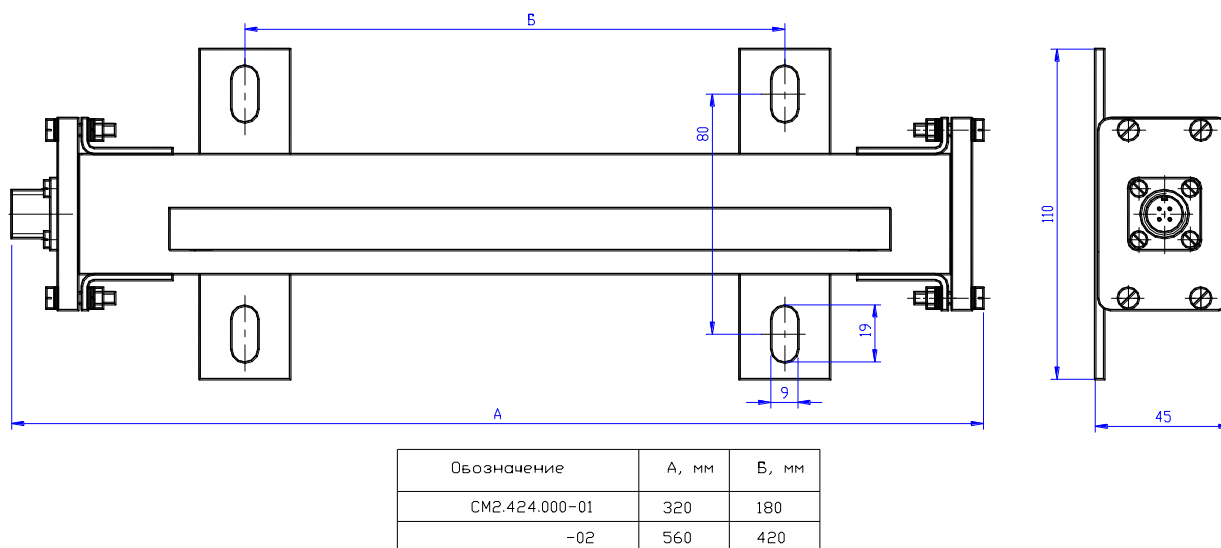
Осветитель ОС СМ2.424.000. Габаритный чертеж
